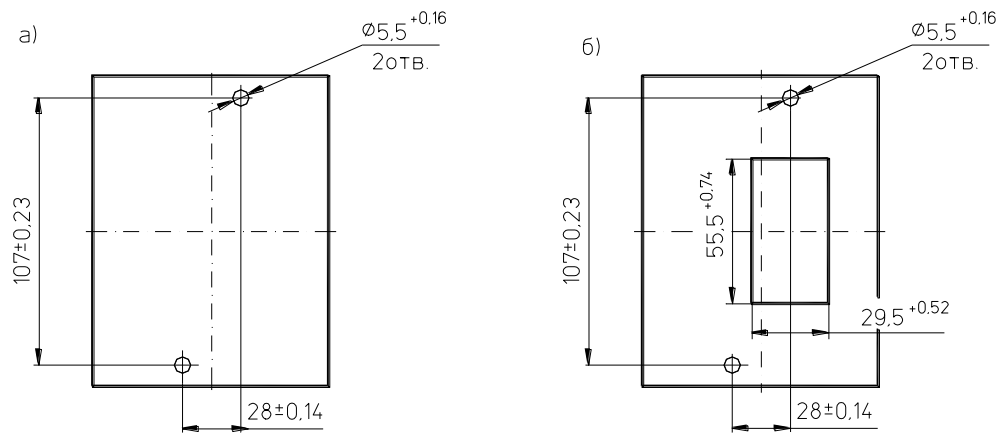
Сверление отверстий под винты крепления однополюсного выключателя в трехполюсном корпусе:
